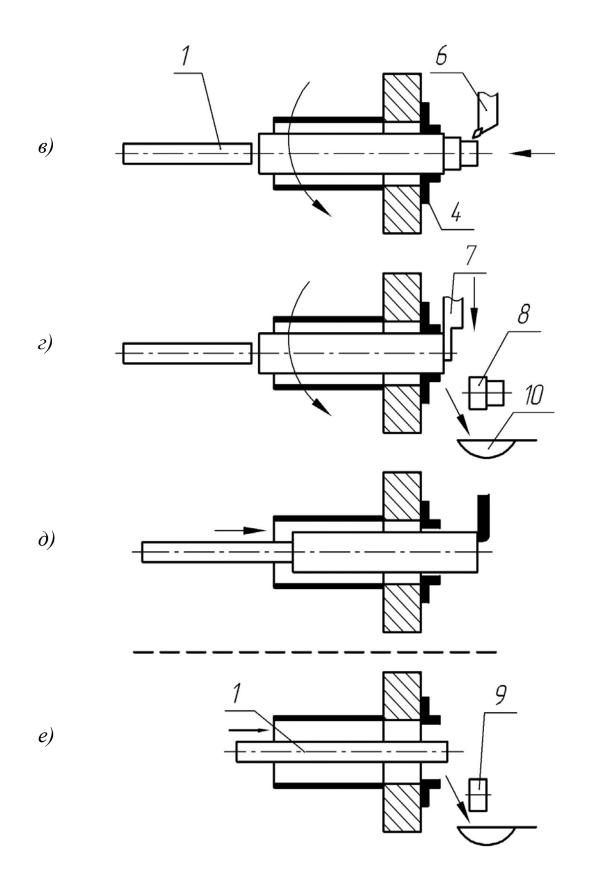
(продолжение). Цикл автоматической работы токарного станка с барфидером: 6 – контурный резец; 7 – отрезной резец; 8 – готовая деталь; 9 – остаток прутка; 10 – ловитель;
